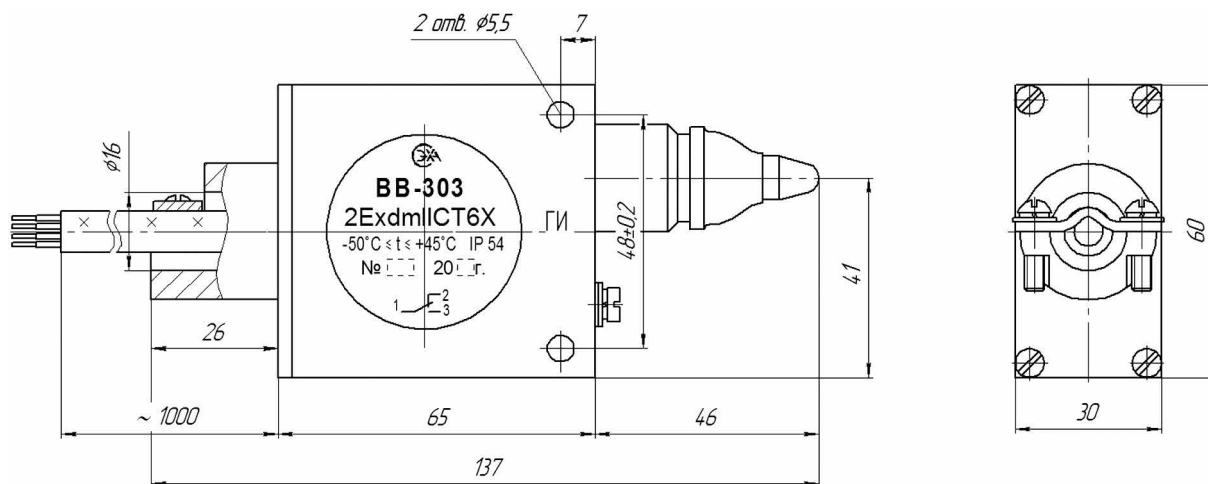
а. Габаритные и установочные размеры ВВ-303
